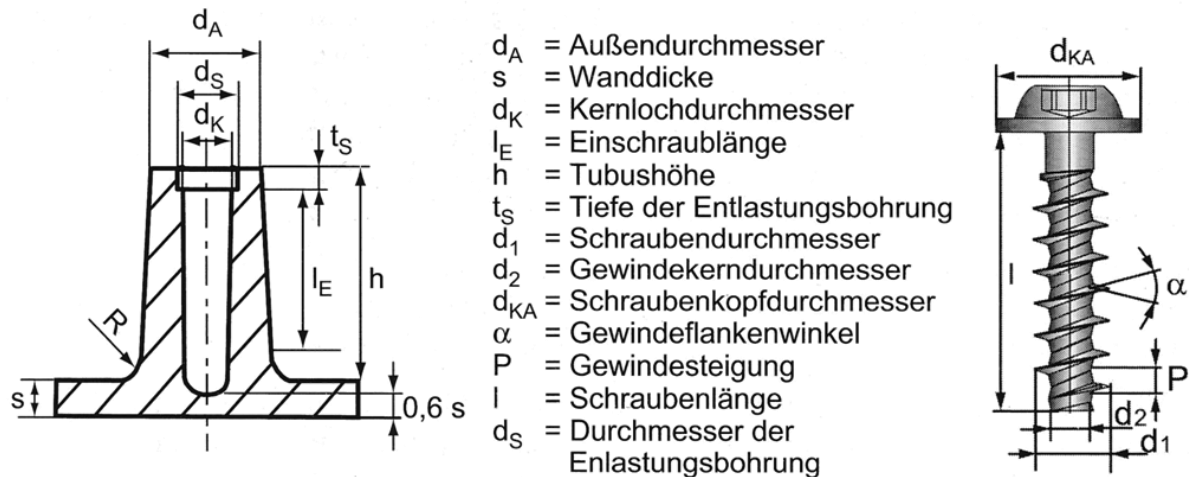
Konstruktive Abmessungen von Einschraubdom und gewindeformender Schraube [33]
